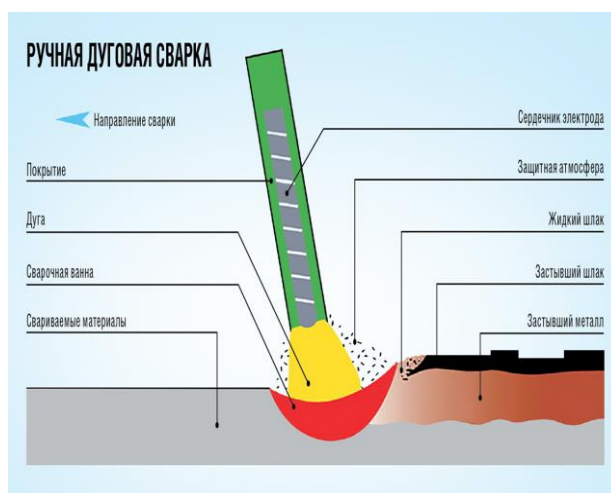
Процесс ручной дуговой сварки (РДС)
